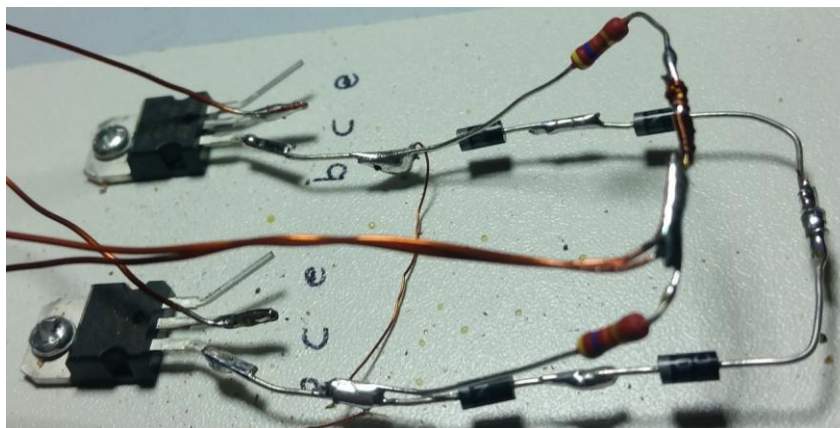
Bobinas do secundário soldadas ao coletor do transistor.
